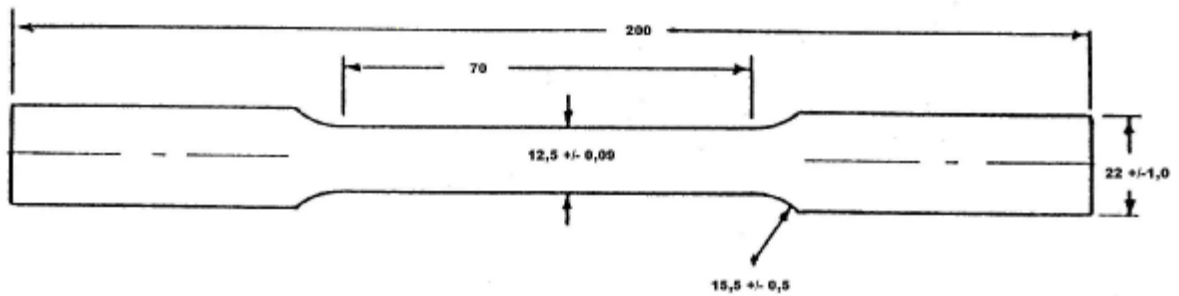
Corpo de prova para o ensaio de tração – Dimensões em mm.
